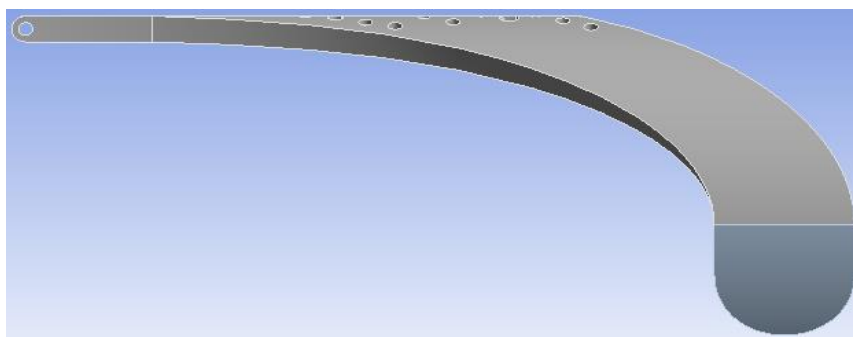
Diseño N°6 eslabon pierna izquierda, vista 2
